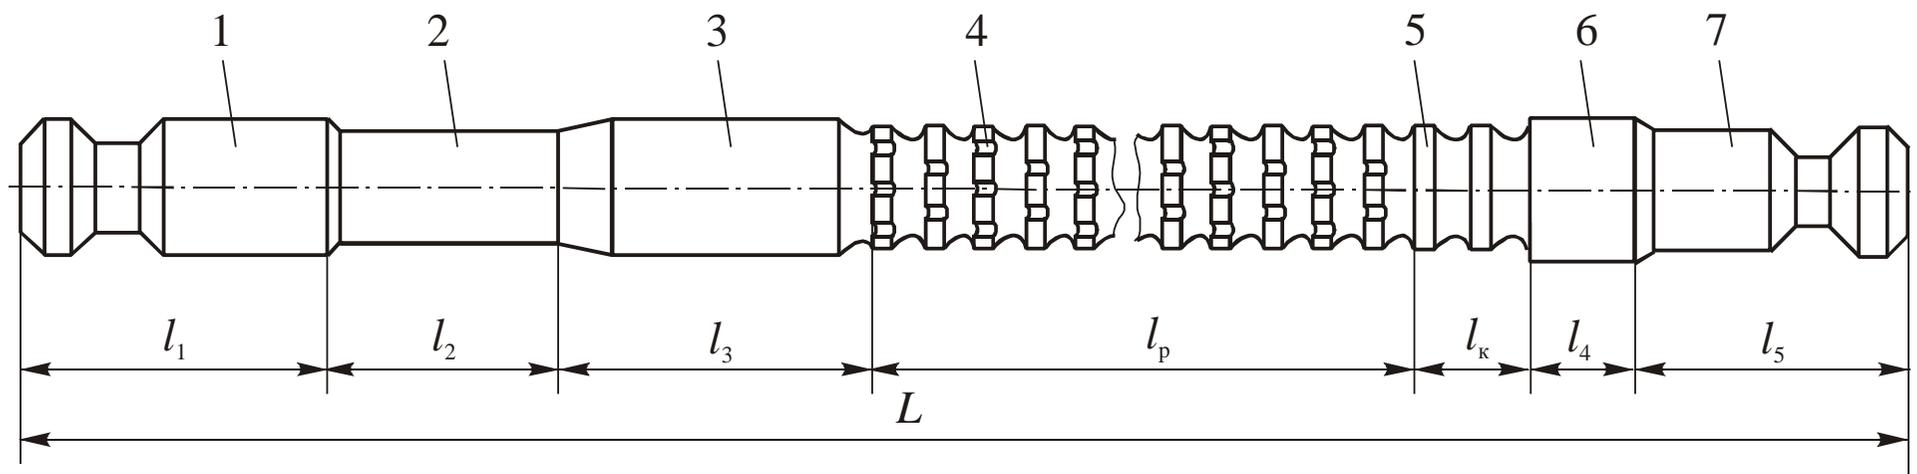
Конструктивные элементы протяжки для обработки отверстий:
